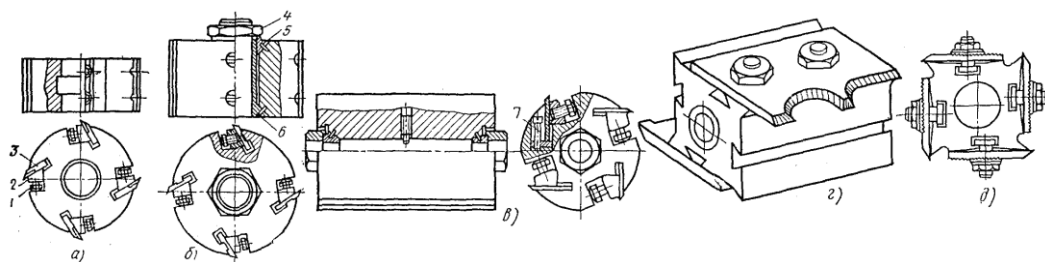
Збірні фрези до чотирибічного поздовжньо-фрезерного верстата: а — з посадкою на вертикальний шпиндель, б, в — з кріпленням на цангах, г, д — квадратні ножові головки; 1 — гвинт, 2 — клин, 3 — ніж; 4 — гайка, 5 — коротка цанга, 6 — довга цанга, 7 — регулювальний гвинт
